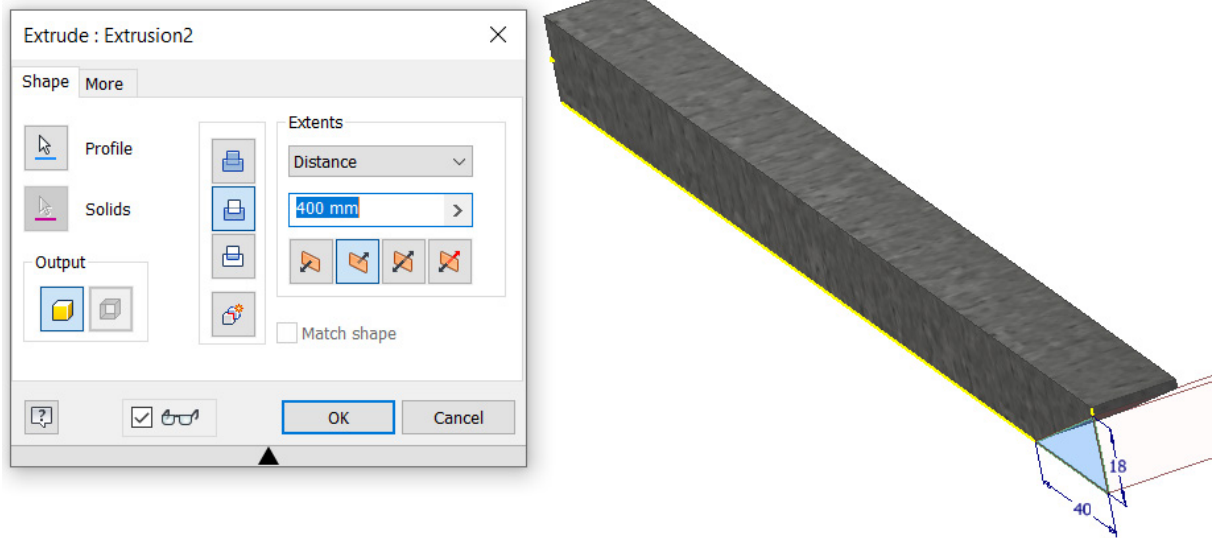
Extrusión de la herramienta de torneado exterior.
